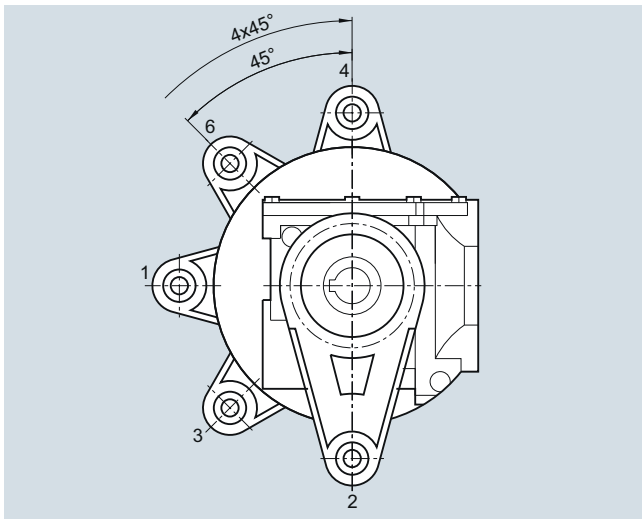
/10 Stirnradschneckengetriebe CAD, Baugröße 29
